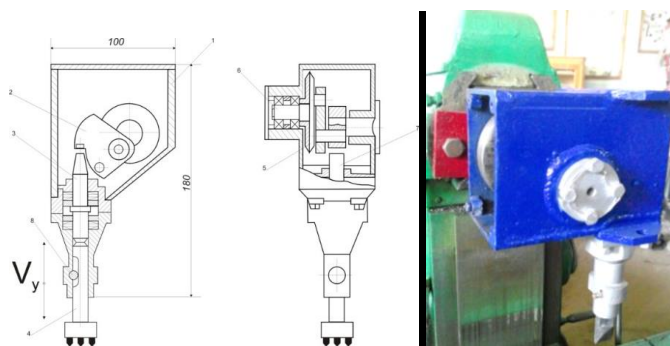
Общий вид ударного узла: 1-корпус; 2-ударник; 3-хвостовик; 4-инструмент; 5-колесо; 6-муфта; 7-букса; 8-фиксатор.
